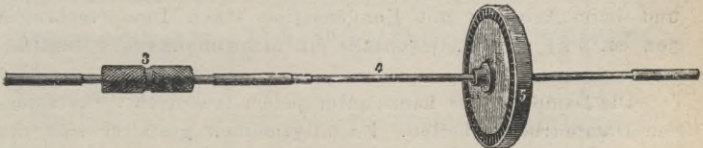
Turbinen-Federwelle mit Schaufelrad und Ritzel.
